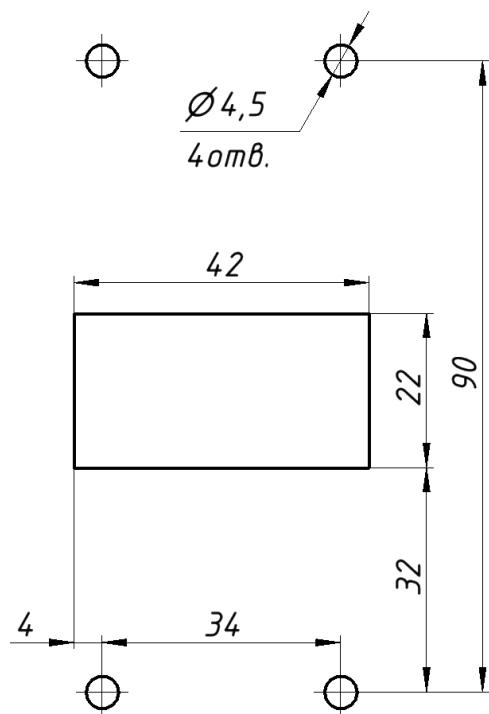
Схема разметки отверстий для установки индикатора положения выключателя
